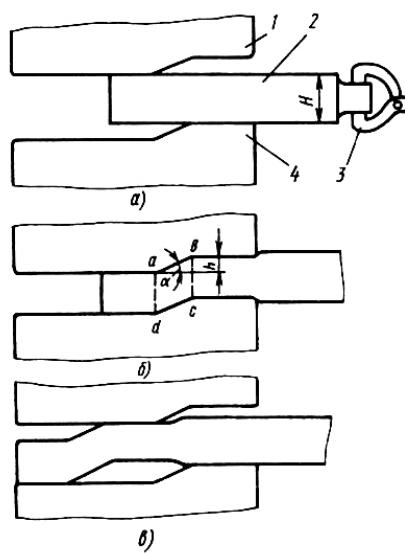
Схема ковки в бойках со ступенчатой рабочей поверхностью:
